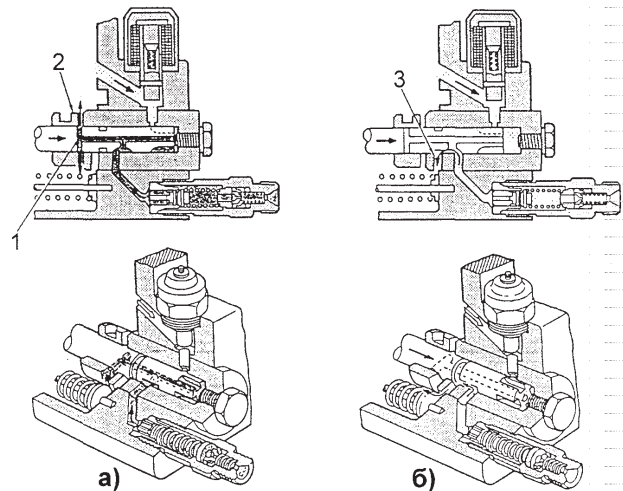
Схема процессов отсечки и слива топлива из ЛВД:
